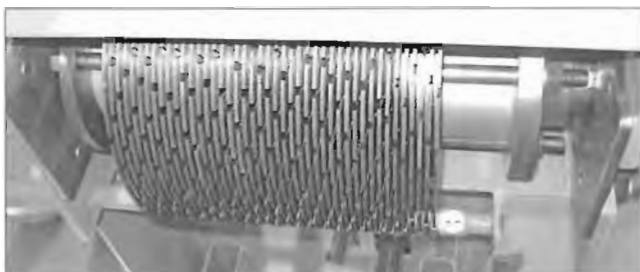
Оснащенный фрезерный вал смонтирован
